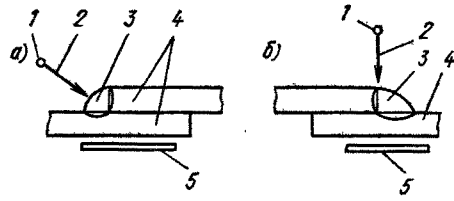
Схемы испытания швов нахлесточных сварных соединений с различным направлением центрального луча (обозначения те же, что и на рис. 11.13)
